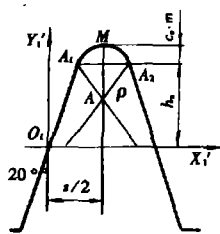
标准渐开线齿条刀具 图 3 渐开线齿轮的齿形
